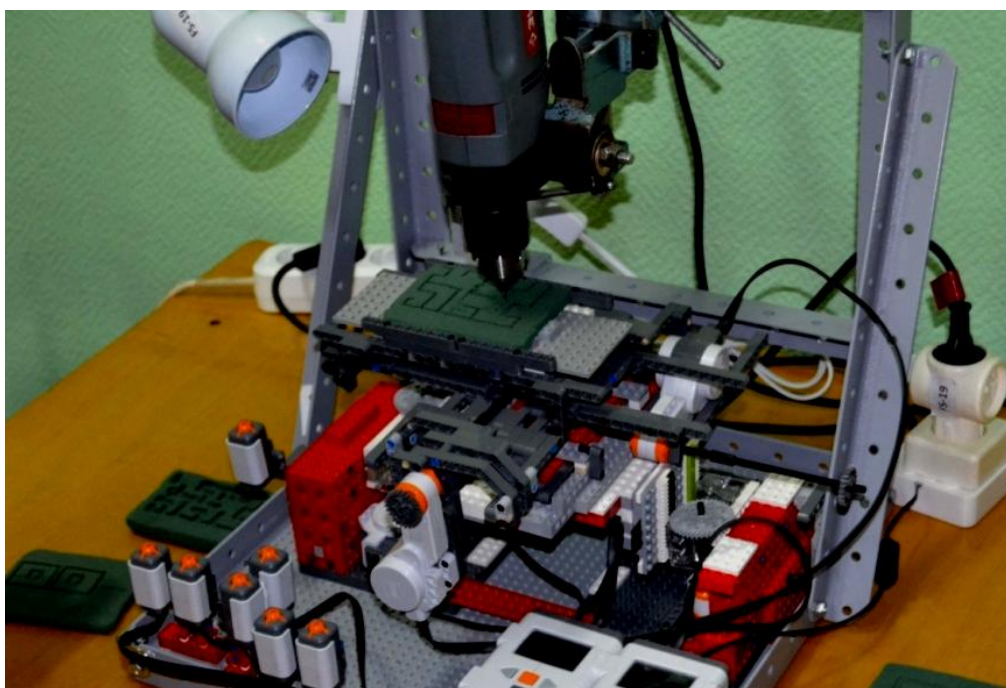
Модель фрезерного станка с ЧПУ, выполненного на базе нескольких конструкторов LEGO Mindstorms [12]
